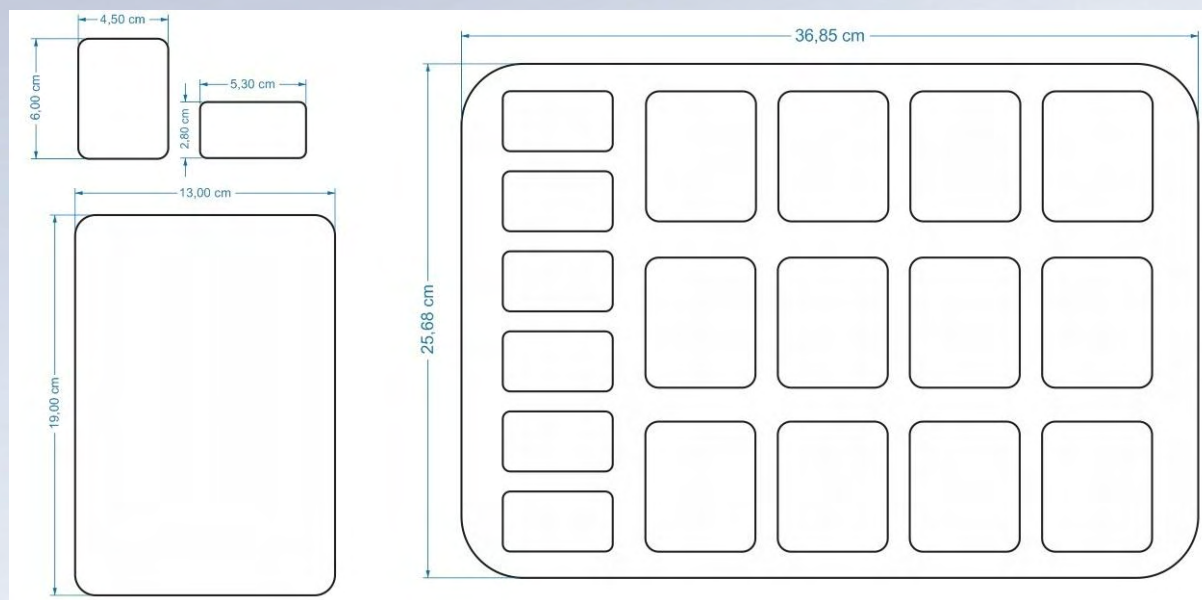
medidas técnicas "elaí para recordar".
